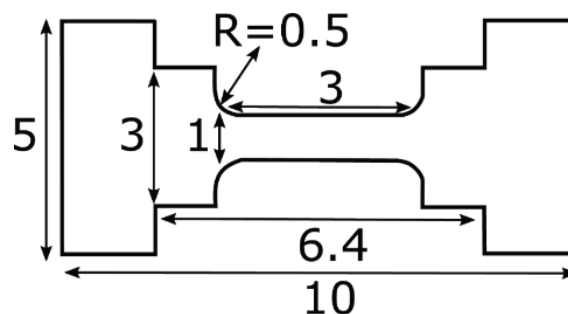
Eprouvette de traction destinée à la machine « Shimadzu » AGS-10kND (unités en mm)
